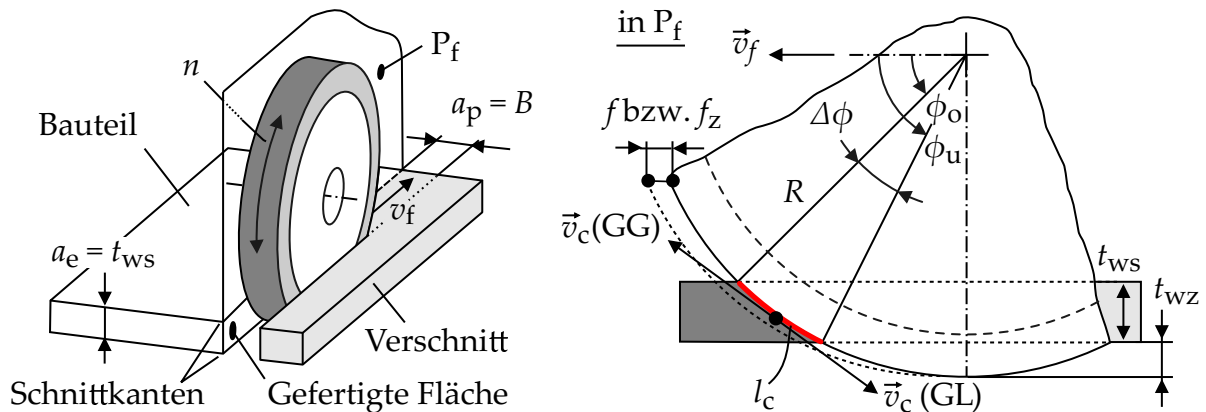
Eingriffskinematik bei der Zerspanung mit scheibenförmigen Werkzeugen
